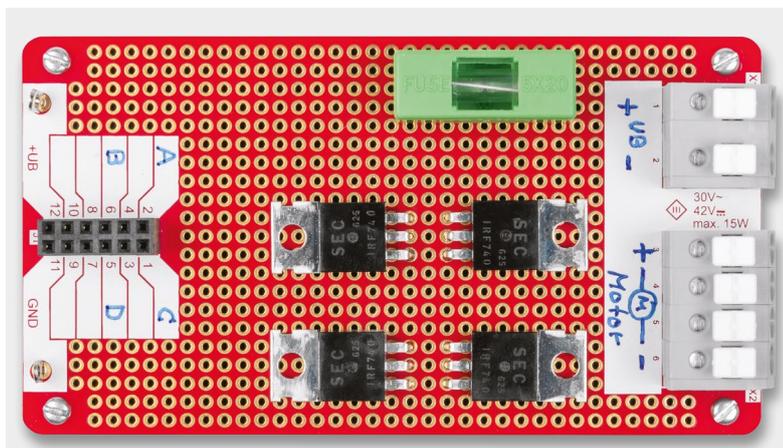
Anwendungsbeispiel mit einer H-Brücke zur Motorsteuerung
